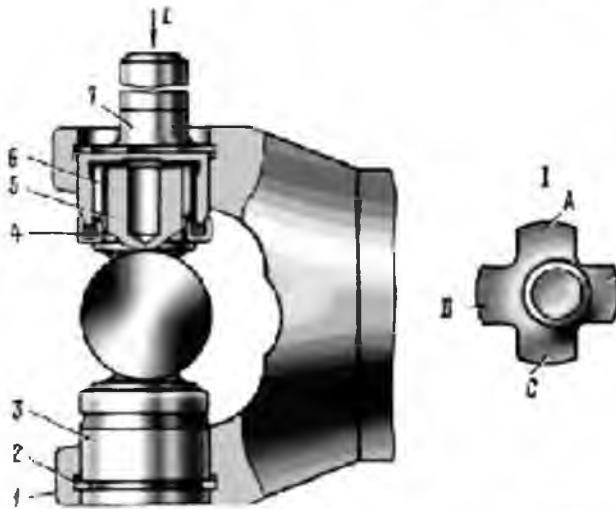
Схема складання карданного шарніра карданної передачі МЕЗ: 1 - вилка карданного шарніра; 2 - стопорне кільце; 3 - корпус підшипника; 4 - сальник; 5 - шип хрестовини; 6 - голка підшипника; 7 - калібр 41.8734.4092; А, В, С, D - пелюстки шупа
